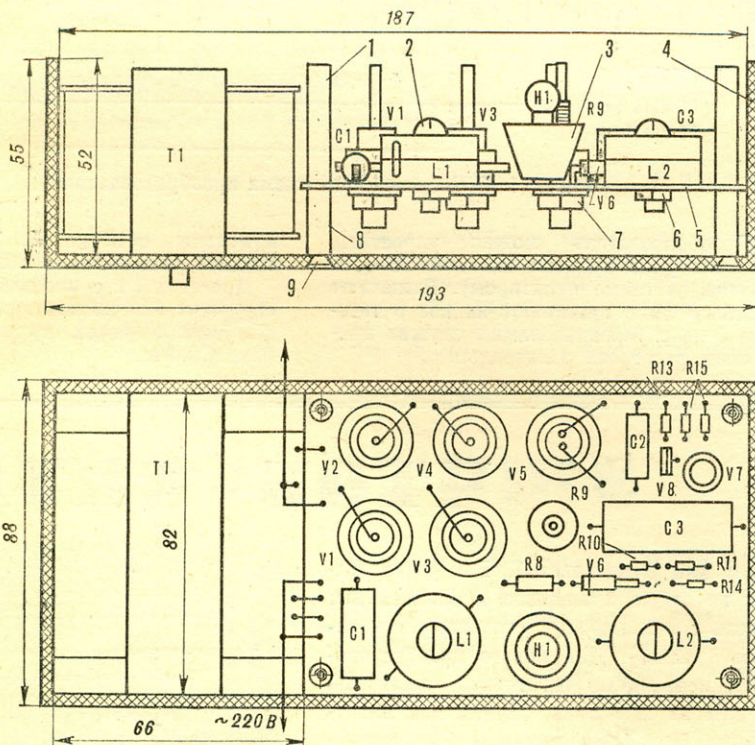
Конструкция терморегулятора: 1 — верхняя стойка, 2 — винт M5×25, 3 — патрон для лампы, 4 — корпус, 5 — монтажная плата, 6 — гайка M5, 7 — гайка M6, 8 — стойка нижняя, 9 — винт M3.
